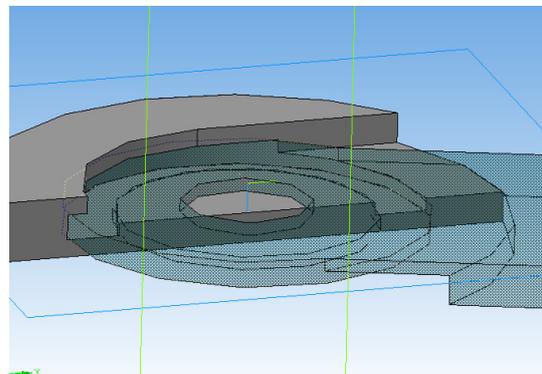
3D модель узла ортеза (в разрезе, вид полупрозрачный)
